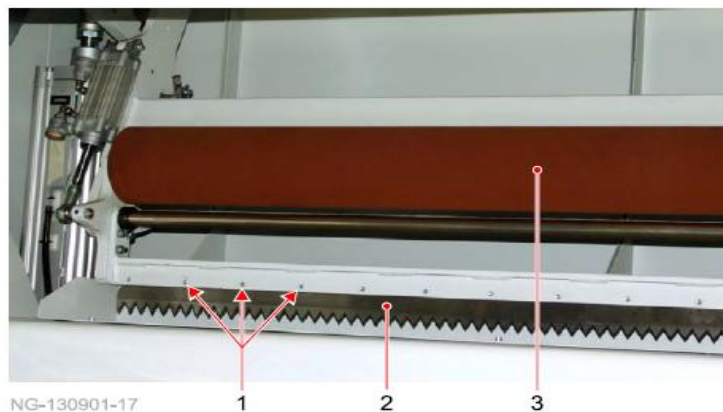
Cuchilla de corte del dispositivo desenrollador.
